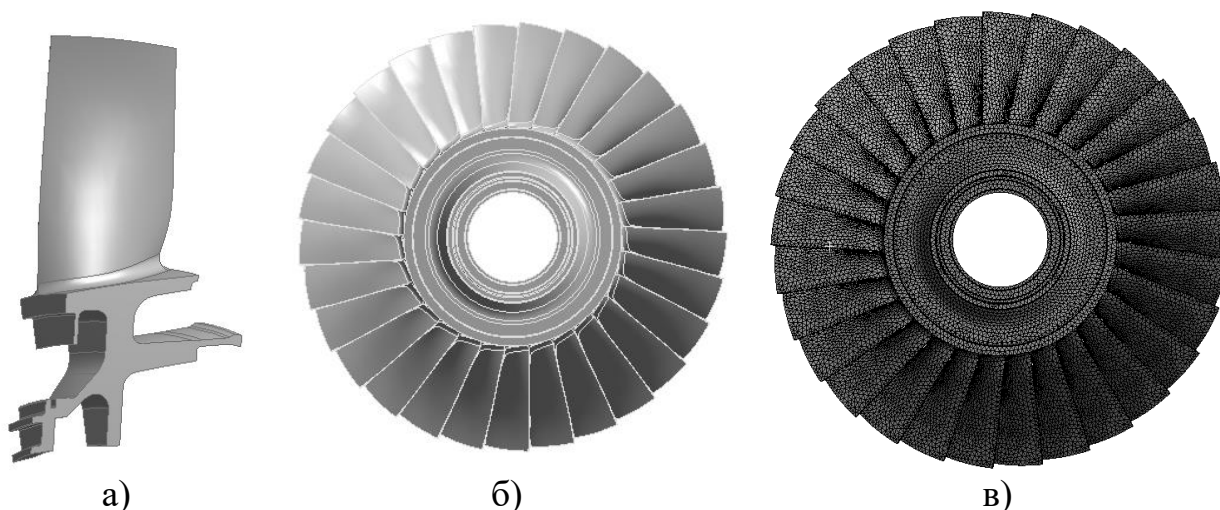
Рабочее колесо фирмы Rolls-Royce с 29-ю лопатками (а – вид одного сектора; б – общий вид, 3D модель; в – КЭМ колеса)
